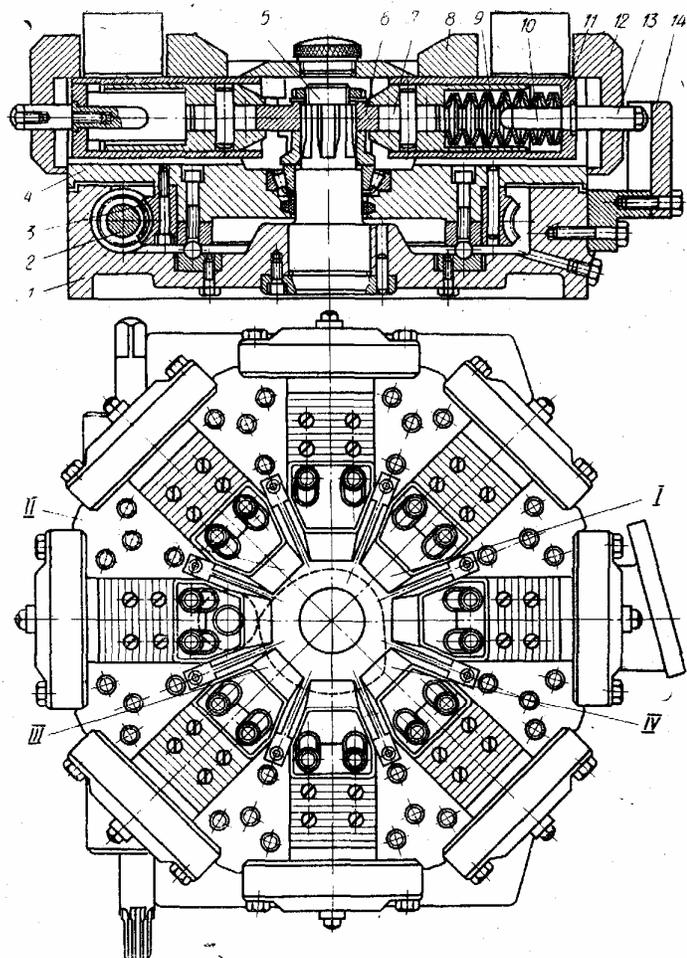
Приспособление для непрерывного фрезерования
